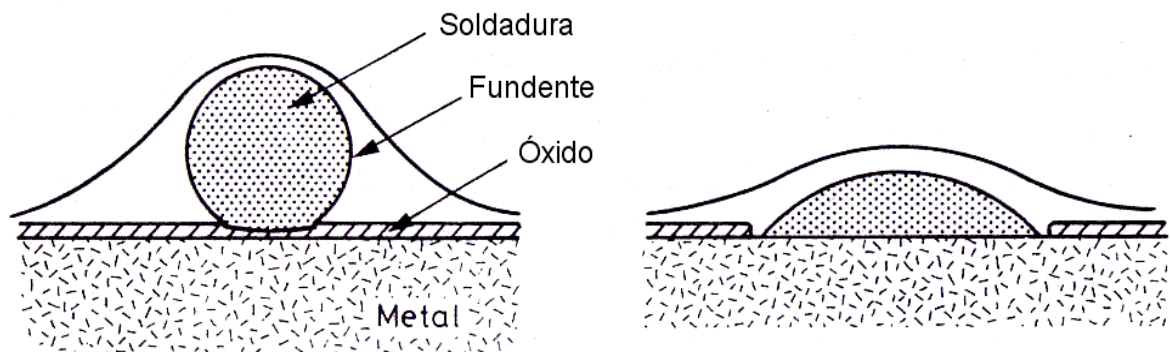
Proceso de esparcimiento de la soldadura.
